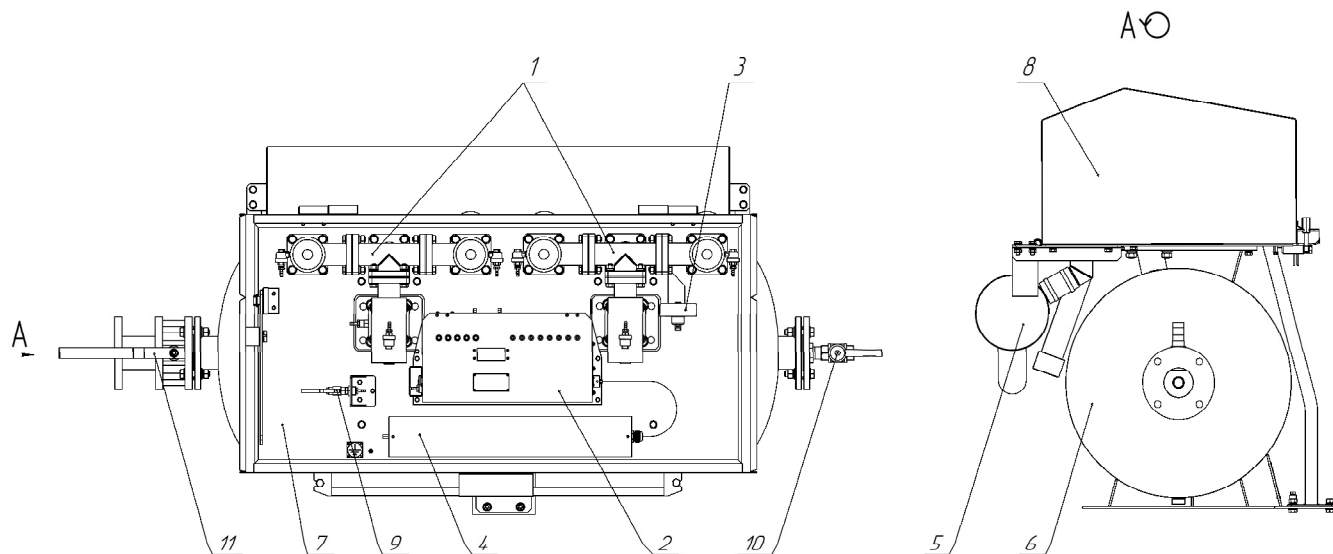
Габаритные и установочные размеры воздухоборника ВУПЗ-15Э
